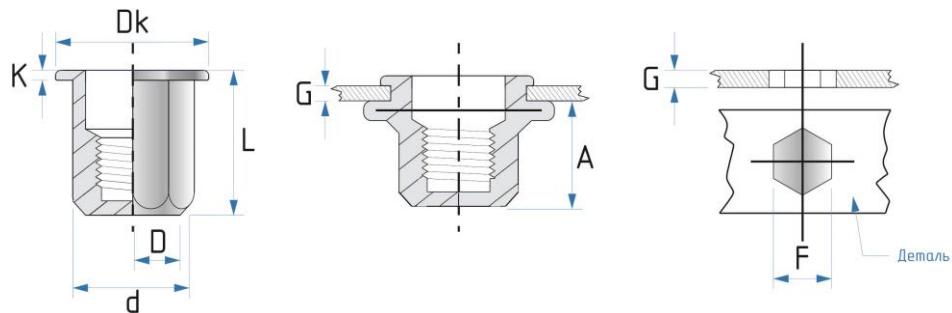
Заклёпка резьбовая шестигранная, закрытая, стандартный борт
